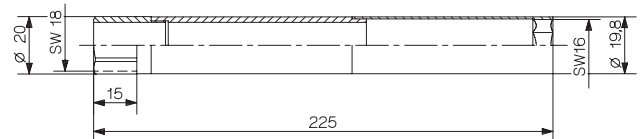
Montagewerkzeug für Sensor Typ 1300A19
